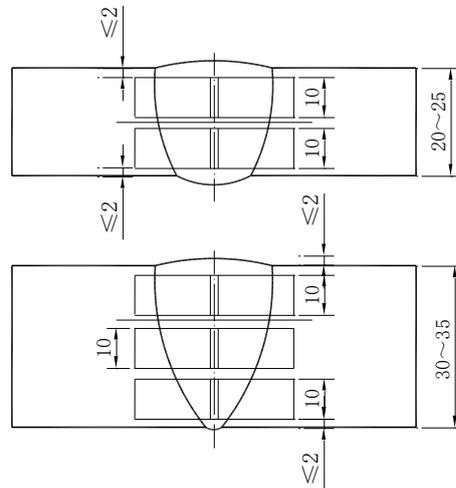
单面焊接双面成型焊接试件的取样位置
